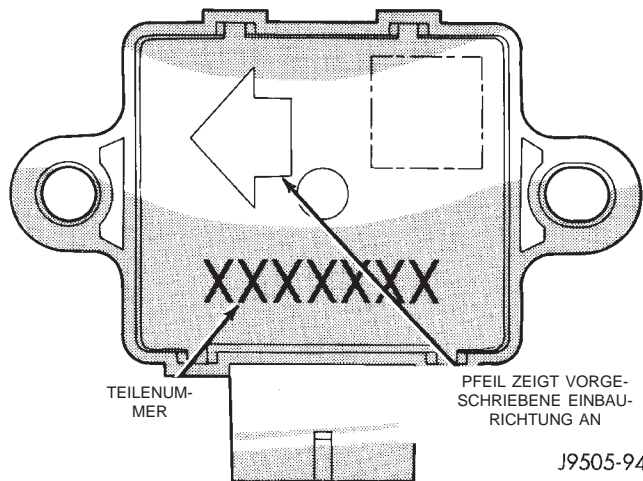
Einbaurichtung des Beschleunigungsschalters
